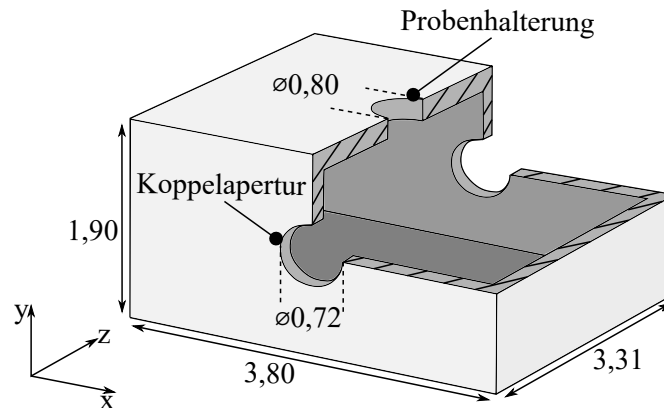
Zeichnung des Hohlraumresonators mit Öffnungen auf der oberen und unteren Seite für die Einführung der LC-Probe. Die Dimensionen sind in mm angegeben.
